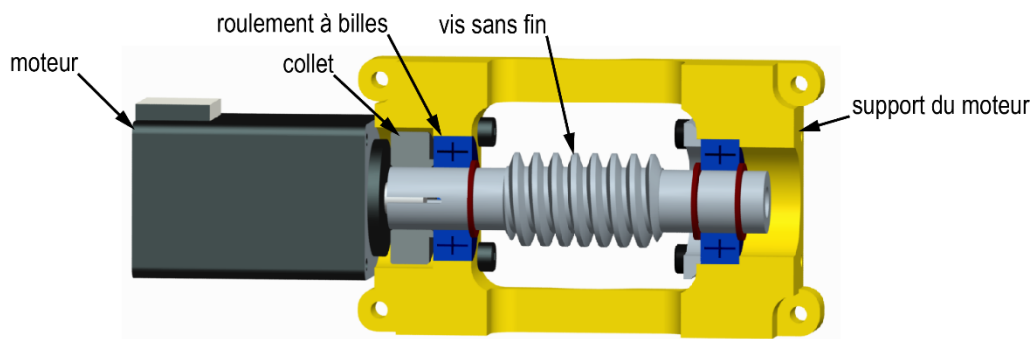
Vue de coupe du sous-assemblage du moteur.
